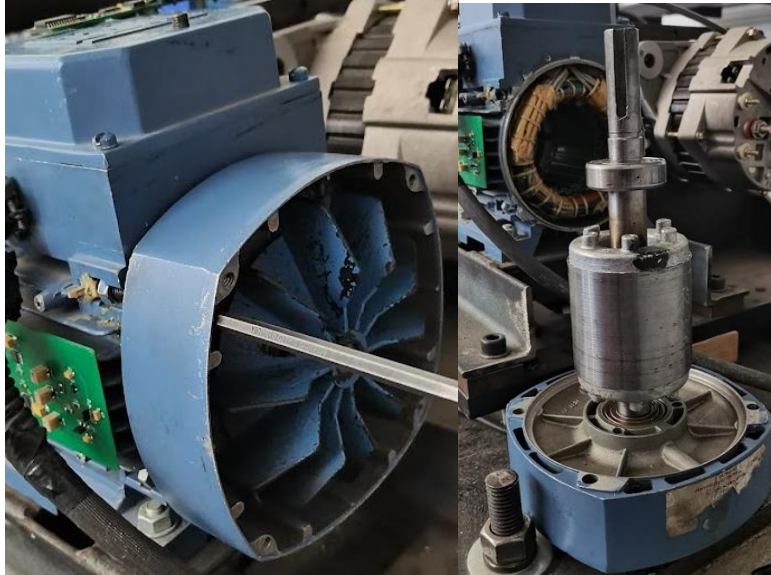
Proceso de desmontaje del rotor (Autoría Propia).
